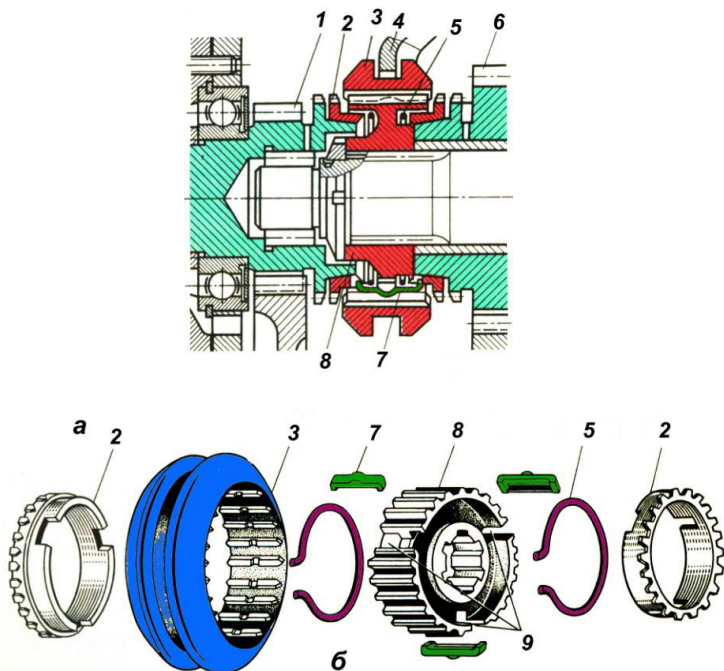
Синхронизатор коробки передач автомобиля ГАЗ-53А:
